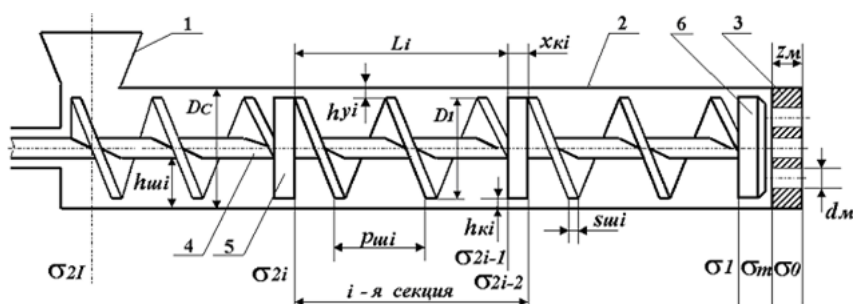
Схема прессующего механизма: 1 – загрузочное устройство; 2 – шнековый цилиндр; 3 – матрица; 4 – шнек; 5 – компрессионный затвор; 6 – головка экструдера
